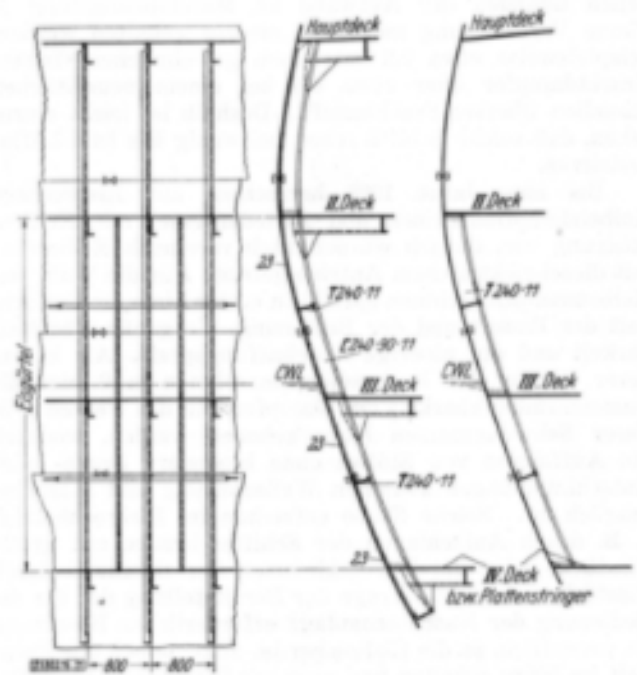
Spantenanordnung. Bild 20 Normales Spant; genietet. Bild 21 Zwischenspant; geschweißt
